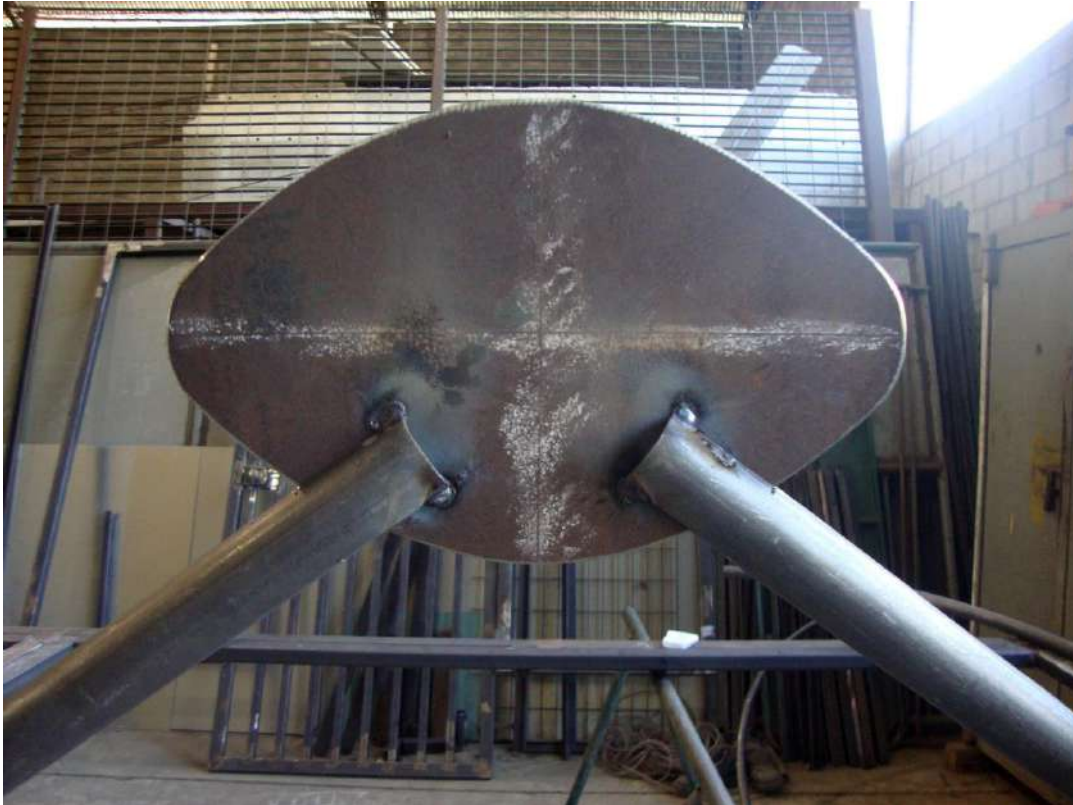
Encaixe da chapa nos tubos ponteados por solda de eletrodo revestido
